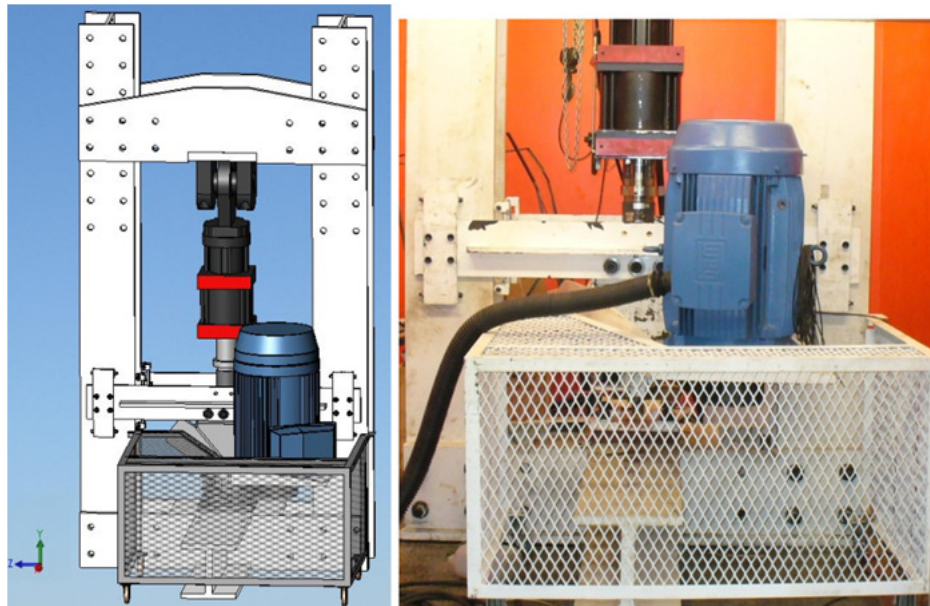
Projeto virtual do equipamento e foto do equipamento fabricado.
